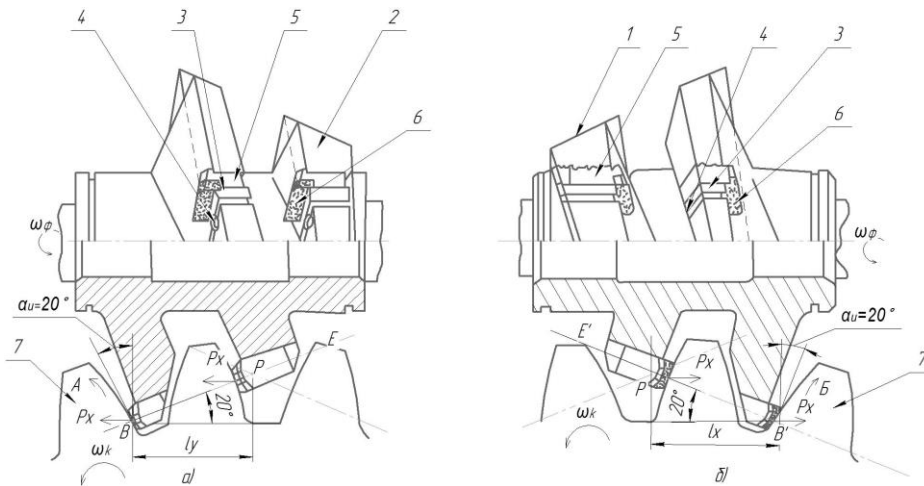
Двокорпусна універсальна фреза одно-стороннього різання: а) – правий корпус; б) – лівий корпус
